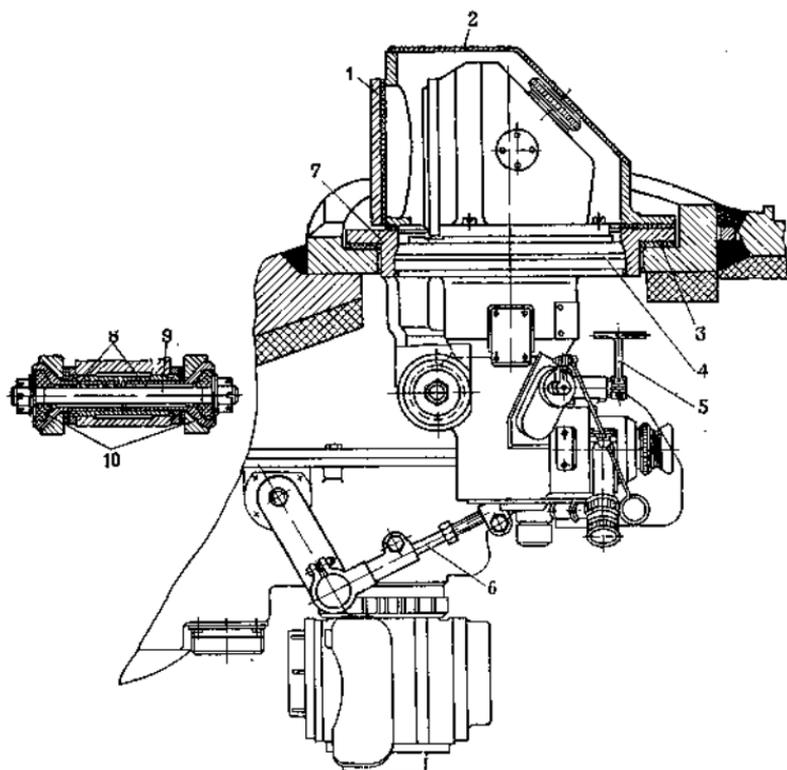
Установка ночного прицела ТПН1-49-23 в машине:
